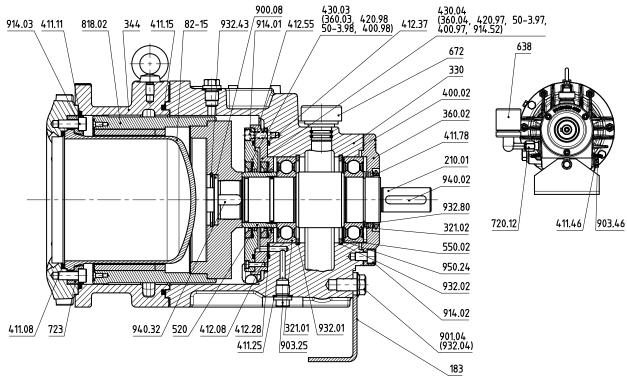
Исполнение подшипникового кронштейна с жидкой смазкой и двойным уплотнительным кольцом вала в качестве защиты от утечек
